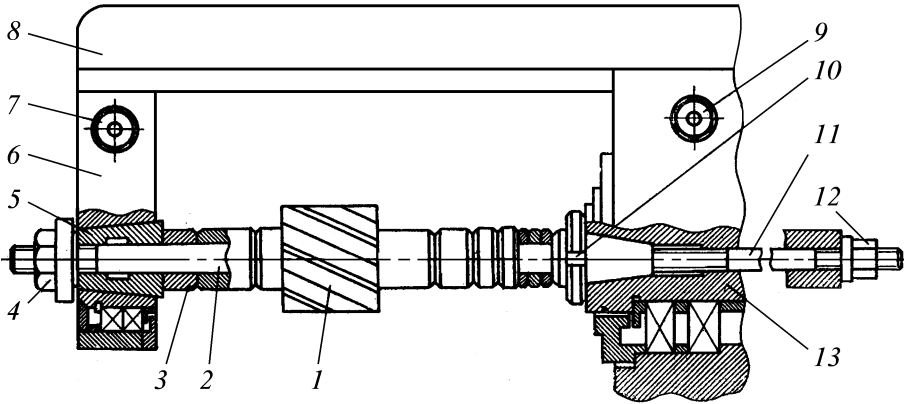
Схема установки и крепления цилиндрической фрезы
